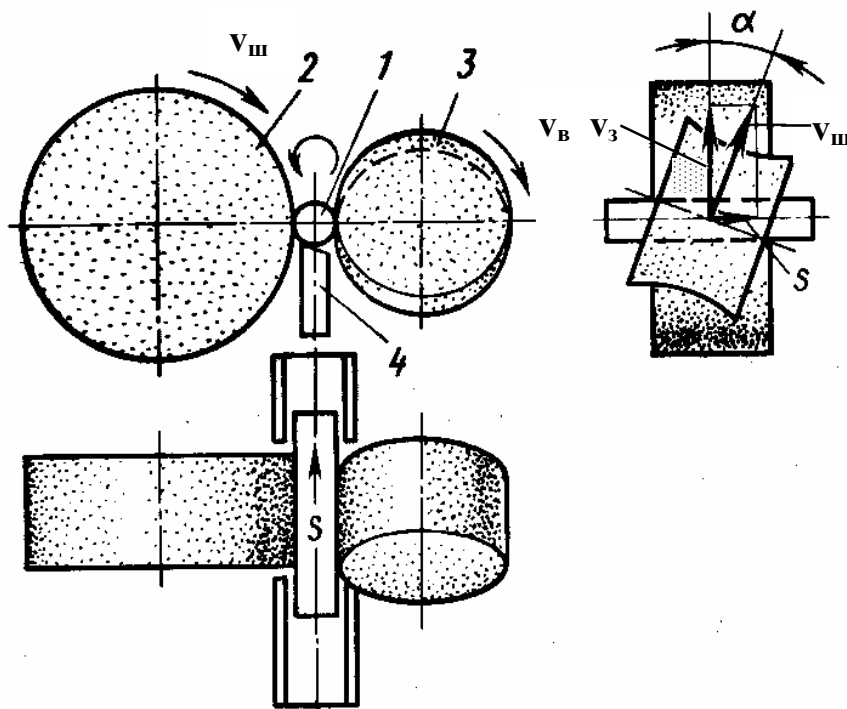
Схема безцентрового круглого шліфування: 1 – оброблювана заготовка; 2 – шліфувальний круг; 3 - ведучий круг; 4 – опорний ніж
